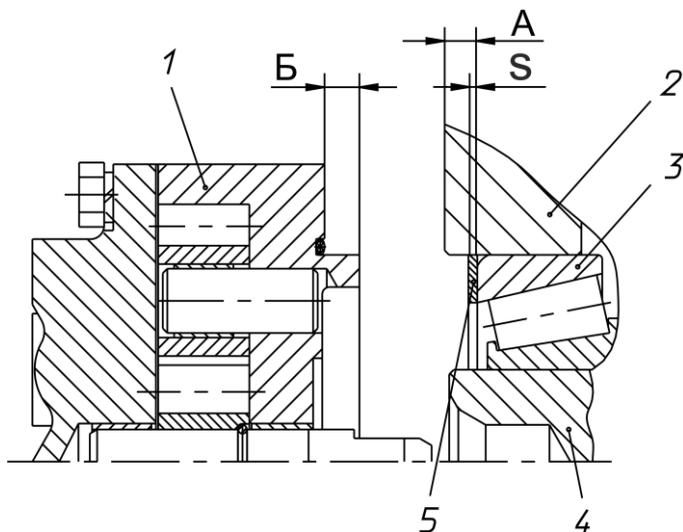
Регулировка осевых зазоров в подшипниках первичного, промежуточного и вторичного валов:
